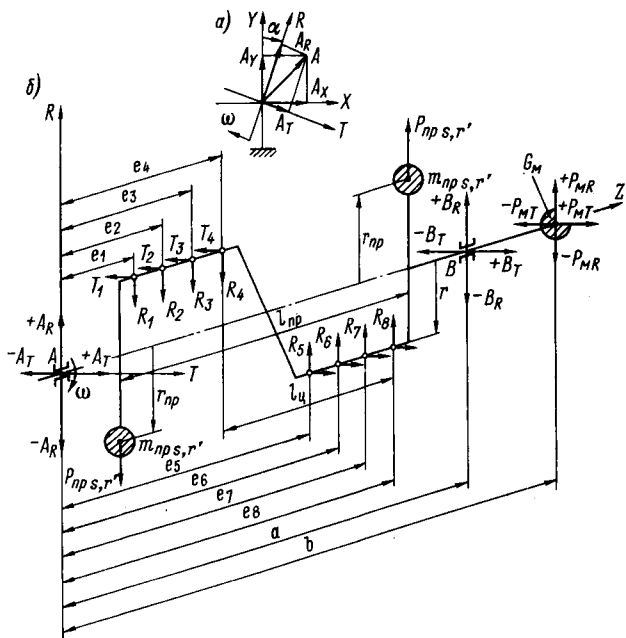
Схема коленчатого вала восьмицилиндрового поршневого компрессора
